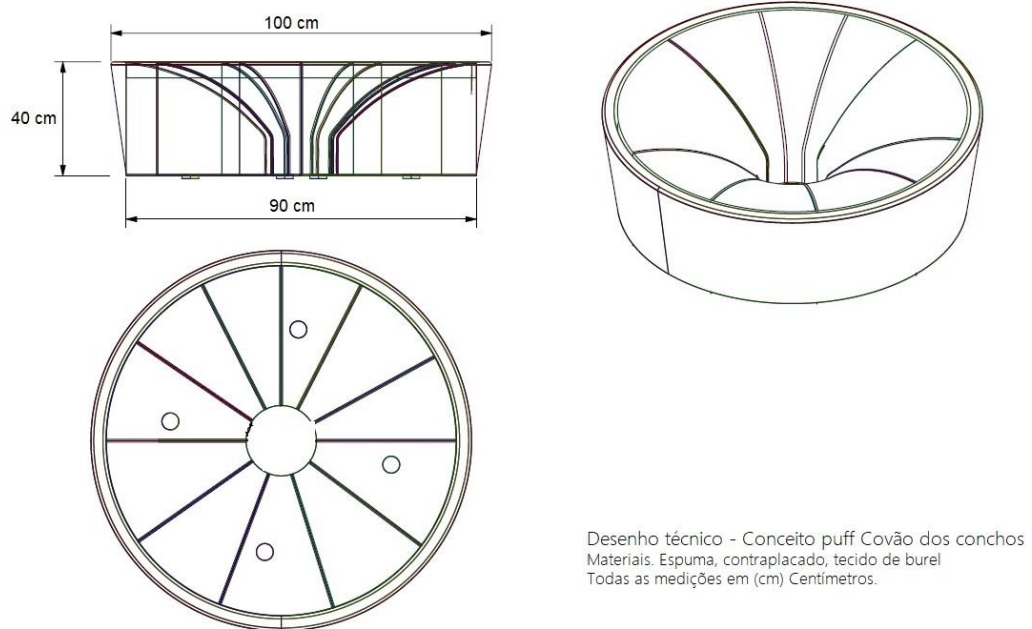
Desenho técnico CAD 3D do puff Covão dos conchos (Fonte: Autor)
